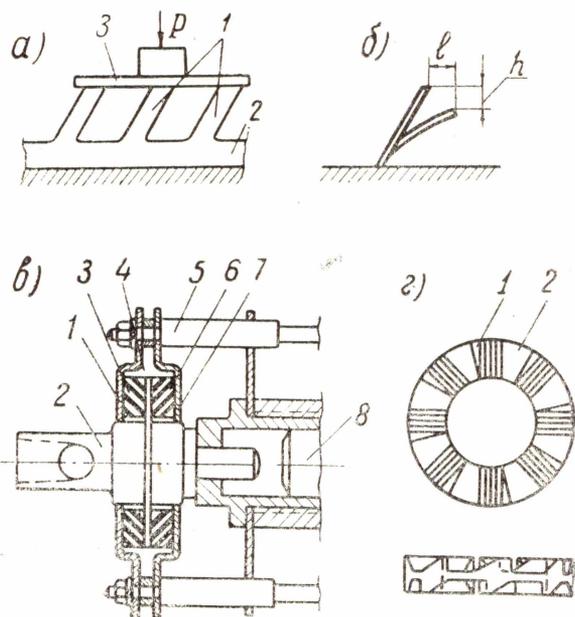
Поворотное устройство фирмы «Синтрон»: а, б—схема зубчатого элемента поворота, в—продольный разрез, г—общий вид шайбы.
